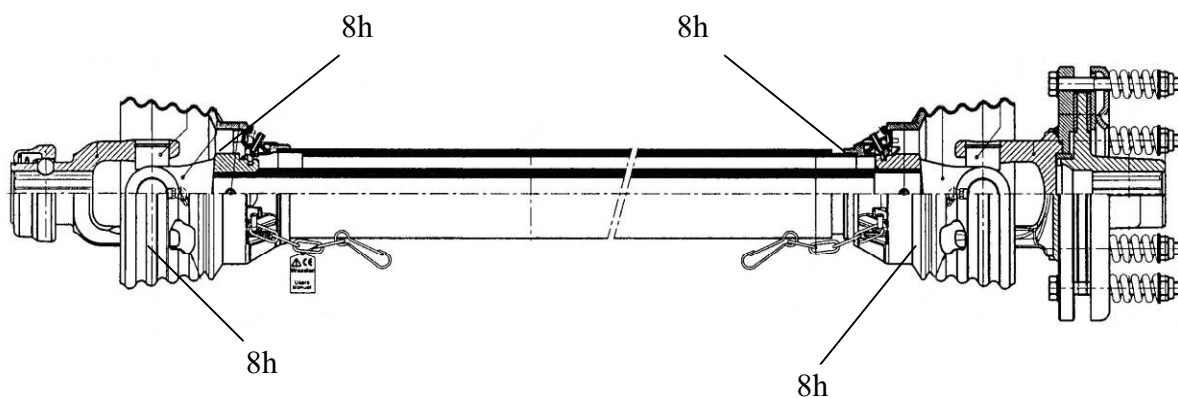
Подсоединение и смазка карданного вала «Weasler».
